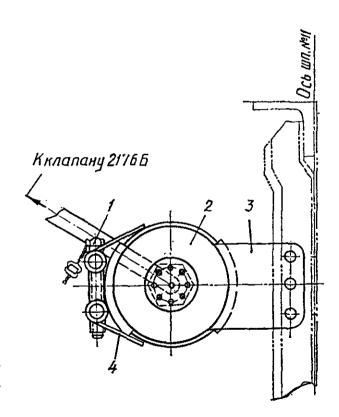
Крепление кронштейна 24-7604-395 и установка фильтра 11ВФ-12-1 переднего выпускного клапана: 1—винт; 2—фильтр 11ВФ-12-1; 3—кронштейн 24-7604-395; 4—хомут 408АН-56
